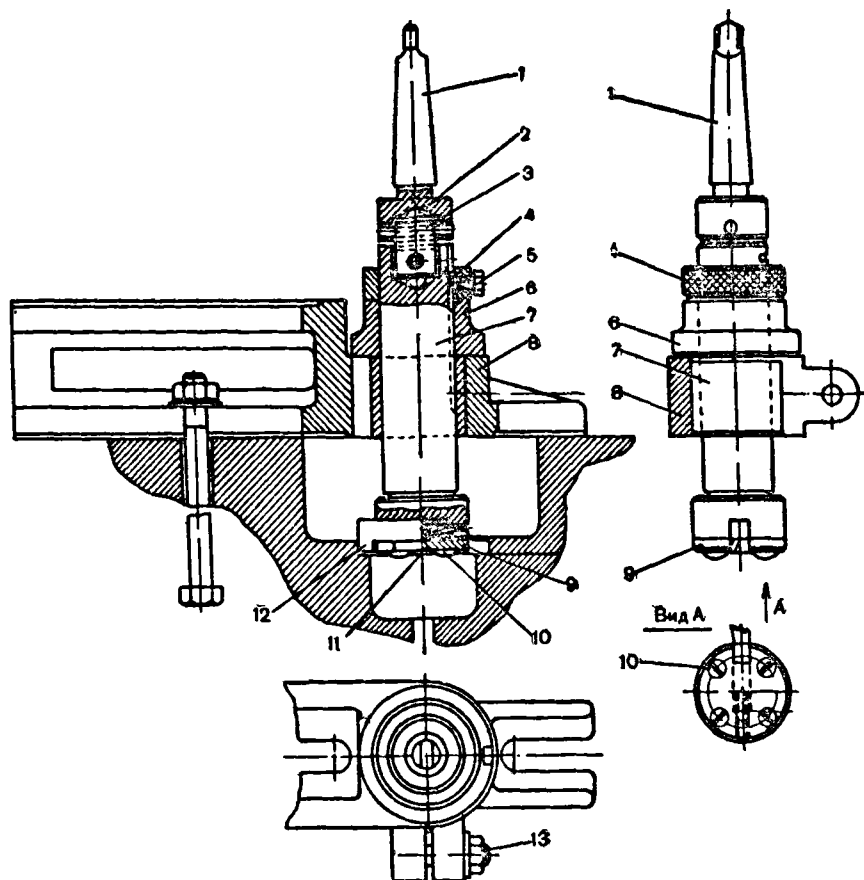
Приспособление для расточки под седло клапана: 1 — хвостовик; 2 — шарик; 3 — сухарь; 4 — кольцо; 5 — стопорный болт; 6 — направляющая втулка; 7 — резцовая оправка; 8 — кронштейн; 9 — зажимная планка; 10 — винт для крепления резца; 11 — винт регулирования вылета резца; 12 — резец; 13 — зажимной болт
